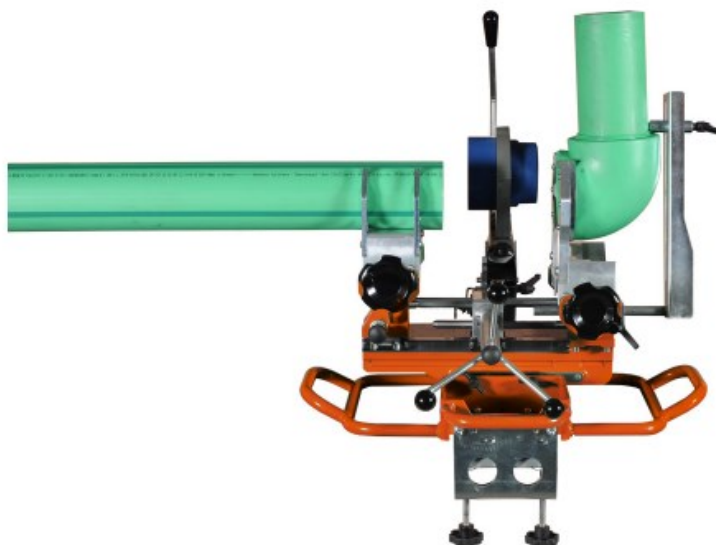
Sidweinder® Compact Jaw Clamp proizvođača McElroy Manufacturing [16]
